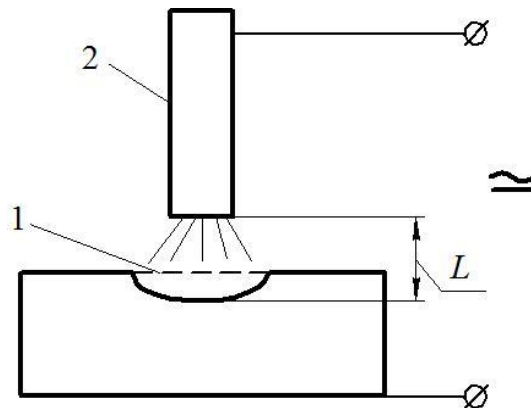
Схематичне зображення процесу зварювання плавким електродом:
